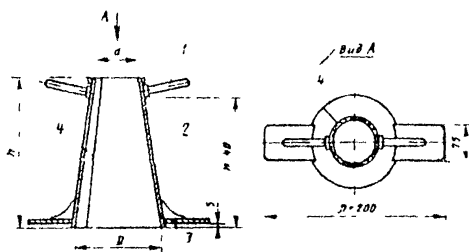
Конус для определения удобоукладываемости бетонной смеси : 1-ручка; 2-конус прибора;3-упоры; 4-сварной шов
